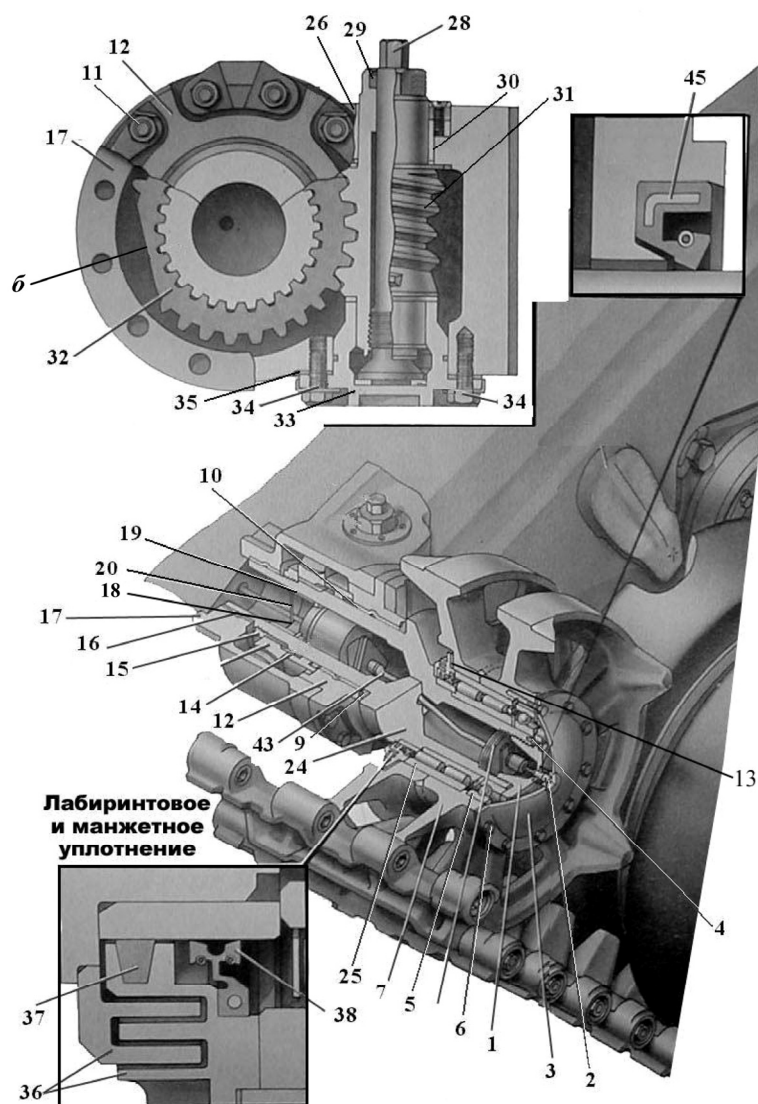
Направляющее колесо с механизмом натяжения: 1 – пробка; 2 – палец; 3, 26 – крышки; 4, 6, 11, 34 – болты; 5 – шарикоподшипник; 7 – направляющее колесо; 9, 27, 29 – резиновые кольца; 10, 16 – латунные вкладыши; 12 – горловина; 13 – уплотнительное кольцо; 14 – распорная втулка; 15 – гайка; 17 – кронштейн; 18 – шплинт; 19, 30 – втулки; 20 – шплинт; 24 – кривошип; 25 – роликподшипник; 28 – стопорный винт червяка; 31 – червяк; 32 – червячное колесо; 33 – опора; 35 – регулировочная прокладка; 36 – кольцо и крышка лабиринтного уплотнения; 37 – войлочный сальник; 38, 45 – манжеты; б – лыска
